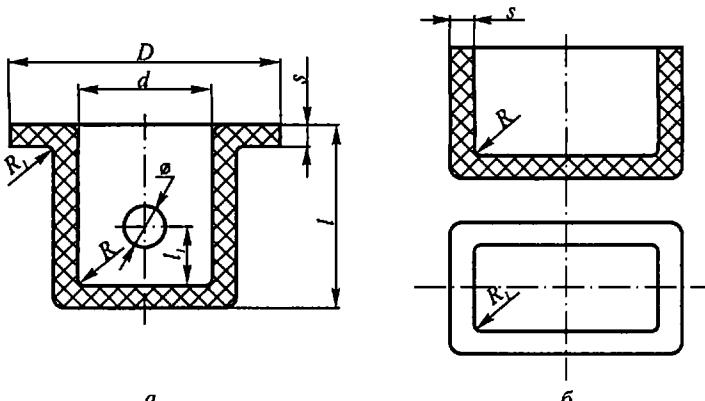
Приклад оформлення кресленика деталі, виготовленої витягуванням
